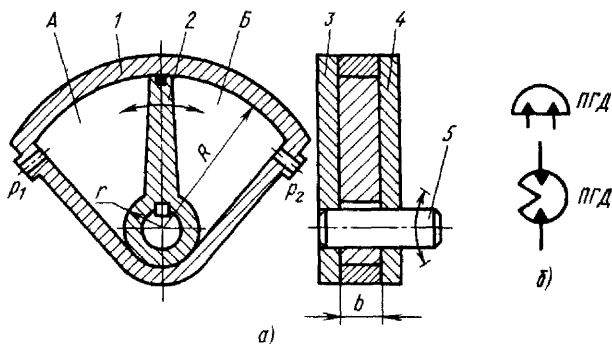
24. Однопластинчатый поворотный гидродвигатель:
